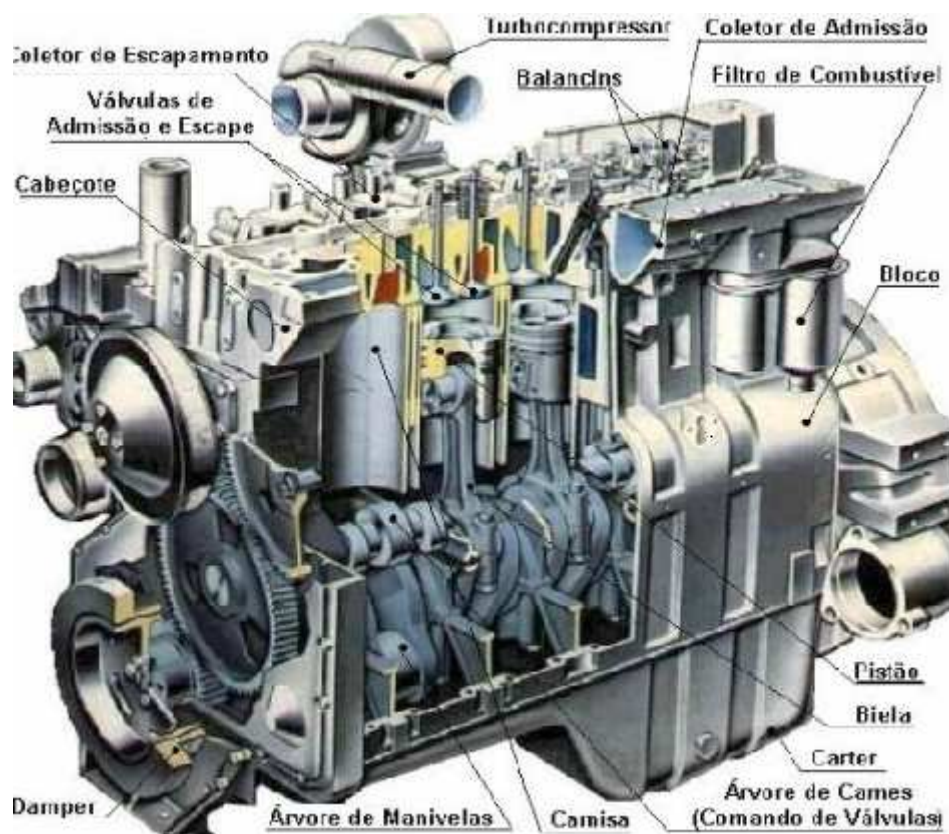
Motor diesel seccionado para mostrar seus componentes
